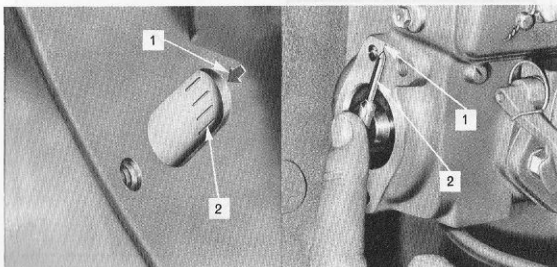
Kontroll av insprutningspumpens inställning (Super Major 5000)
